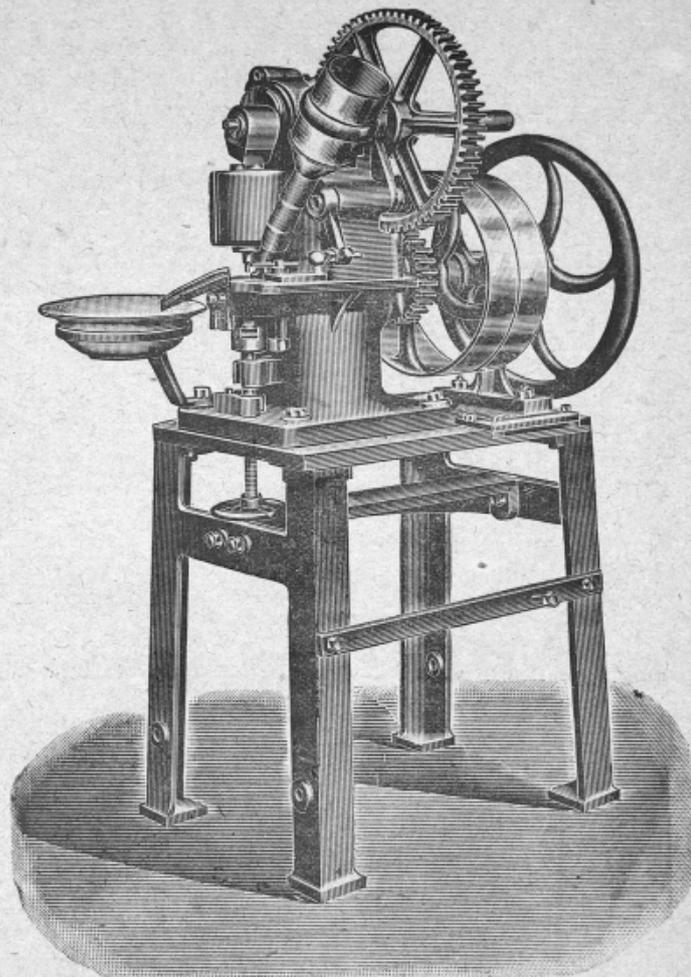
Machine à comprimer grand modèle. Pouré et Sauton.
